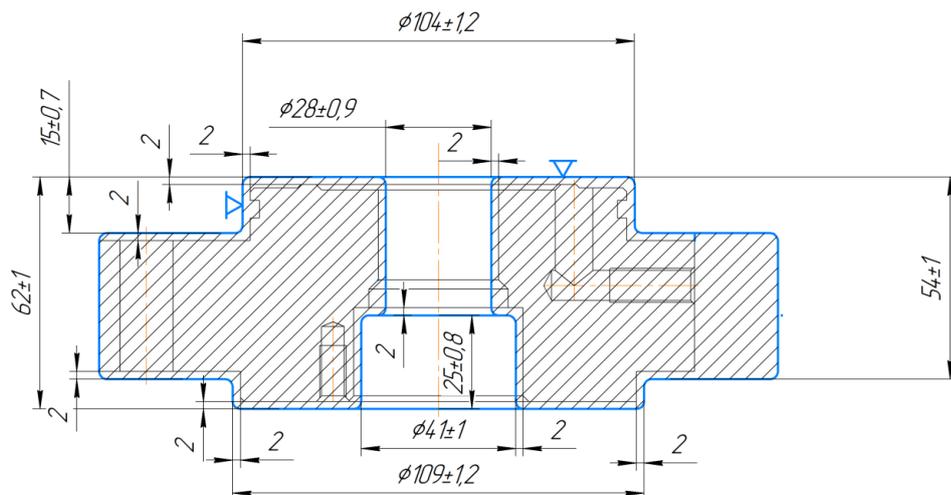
Чертеж заготовки для детали «Крышка передняя»
